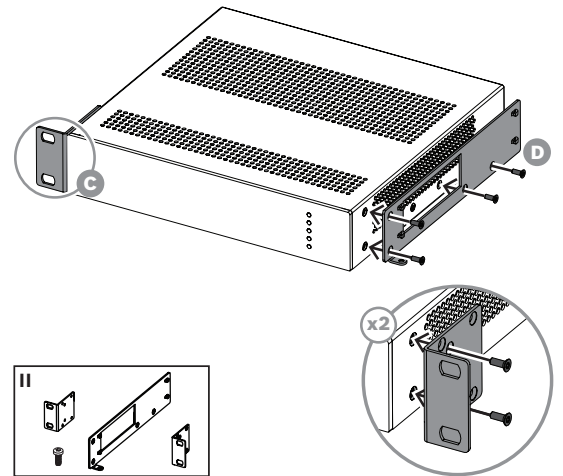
collegamento delle staffe per rack e della piastra di fissaggio (U120:1/U240:1)
